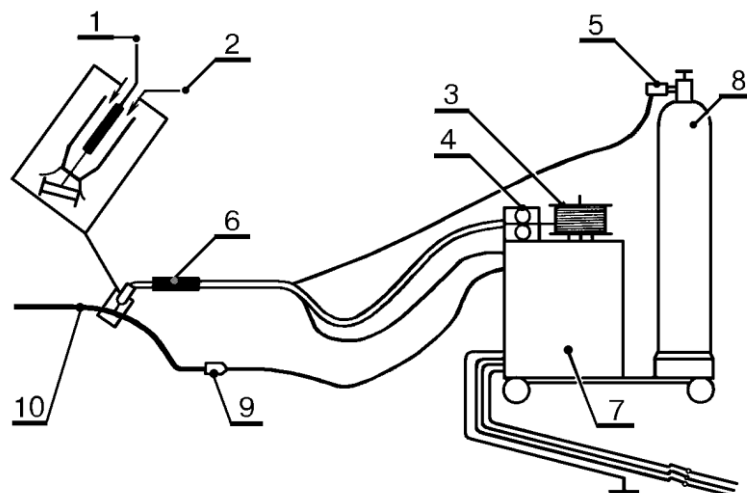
Схема напівавтоматичної установки для MIG/MAG зварювання
